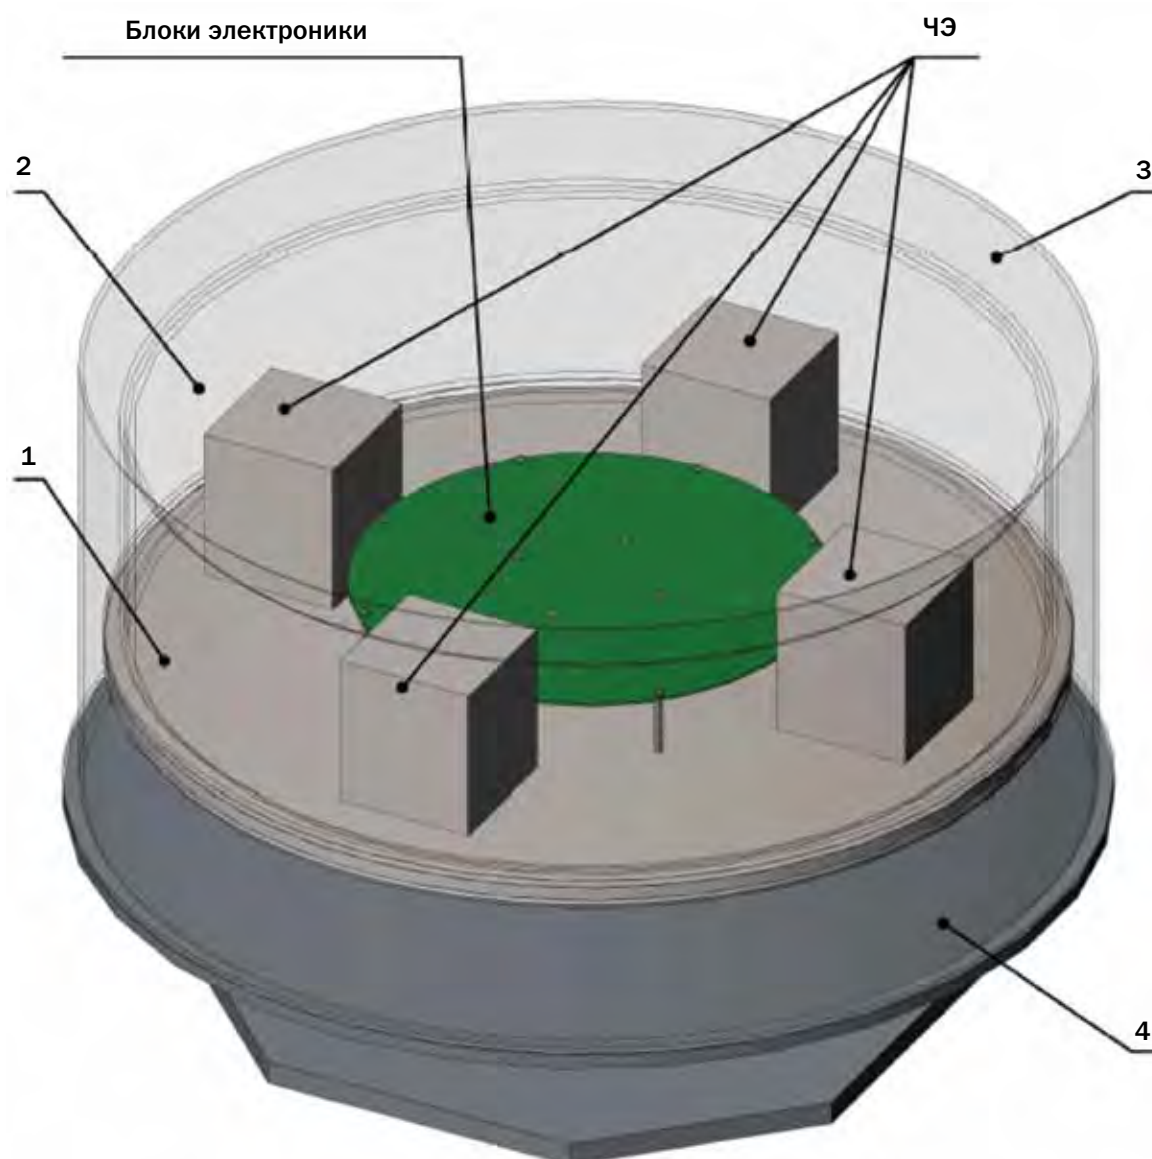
Общий вид конструктивной схемы макета роторного ГГ
